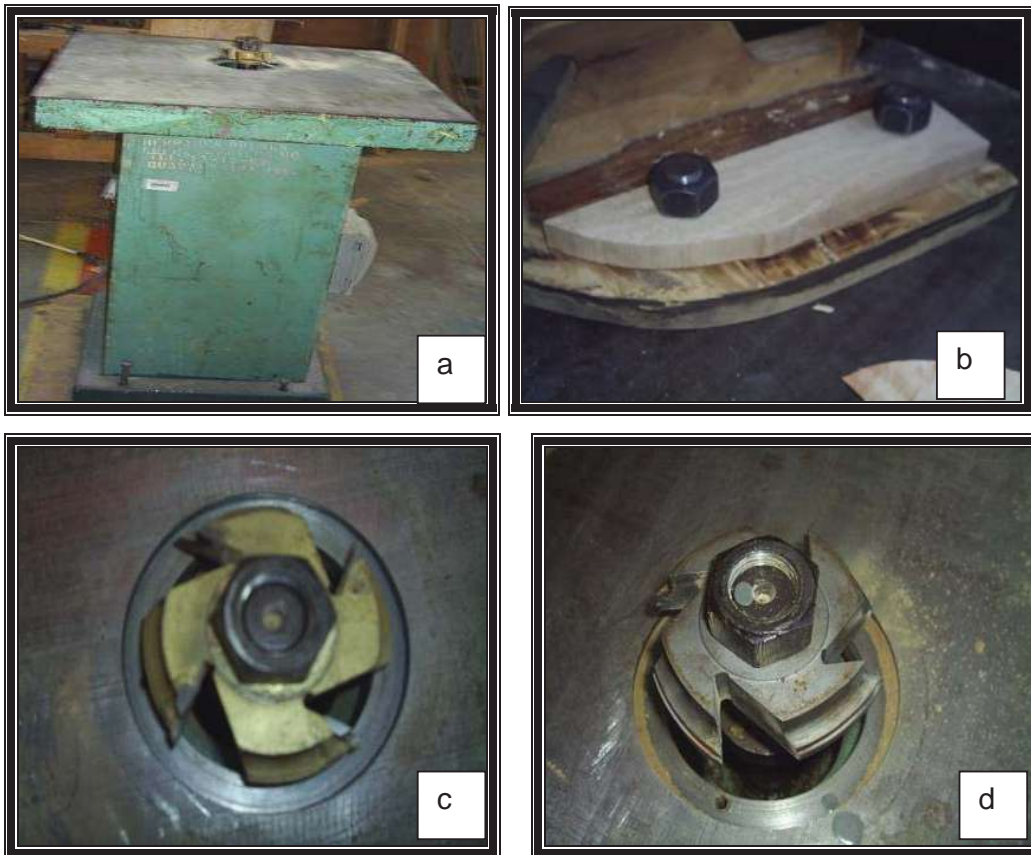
Equipo utilizado en la prueba de moldurado; a) Trompo utilizado en la prueba; b) Plantilla usada; c) Frese de carburo de tungsteno; d). Fresa de acero a alta velocidad.
